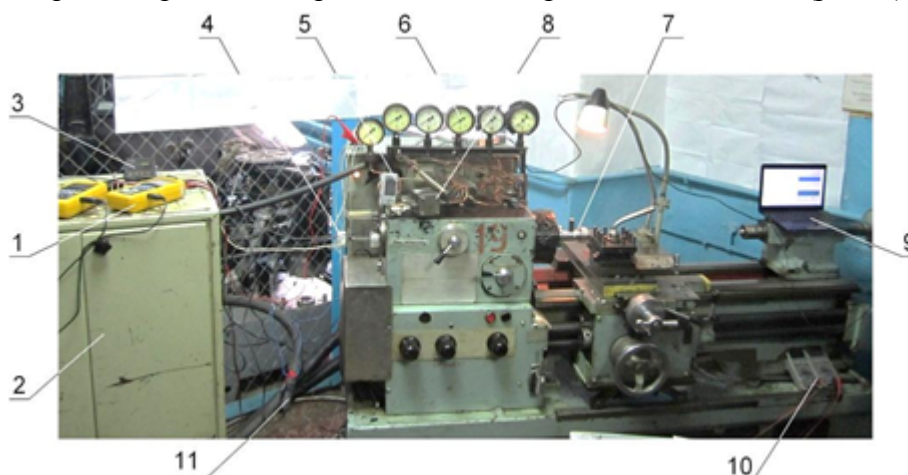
Ескіз верстатного пристрою для оброблення симетричних заготовок:
